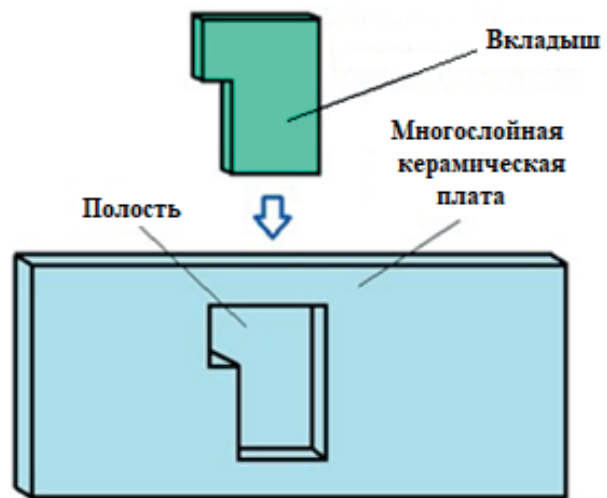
Схема укладки вкладыша в керамическую заготовку
